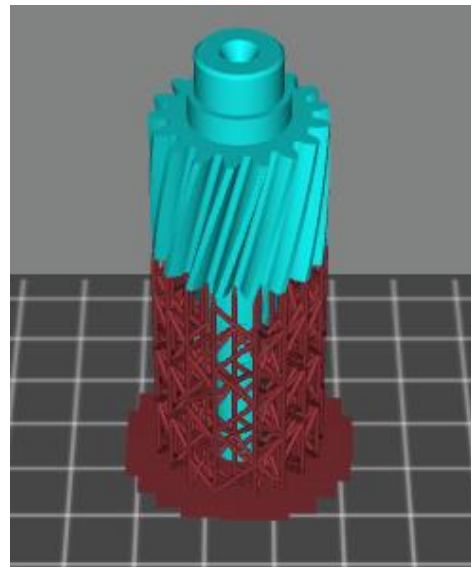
Опорні конструкції для 3D друку зубчастих коліс
